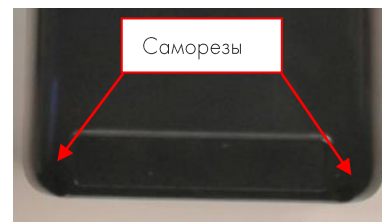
Саморезы, фиксирующие корпус СТ.
